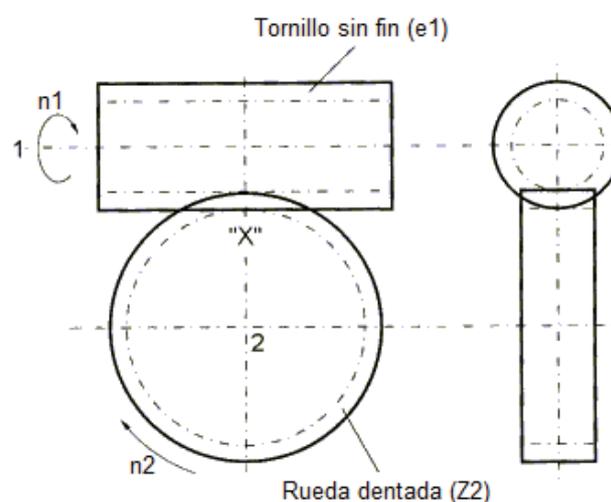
Sistema de tornillo sinfín y rueda dentada. (Engranajes, 2013)
